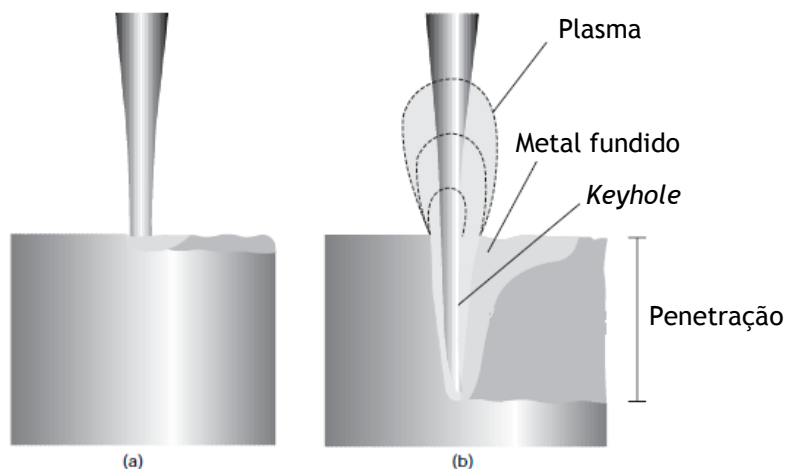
Modos de soldadura por laser: a) condução; b) *keyhole
